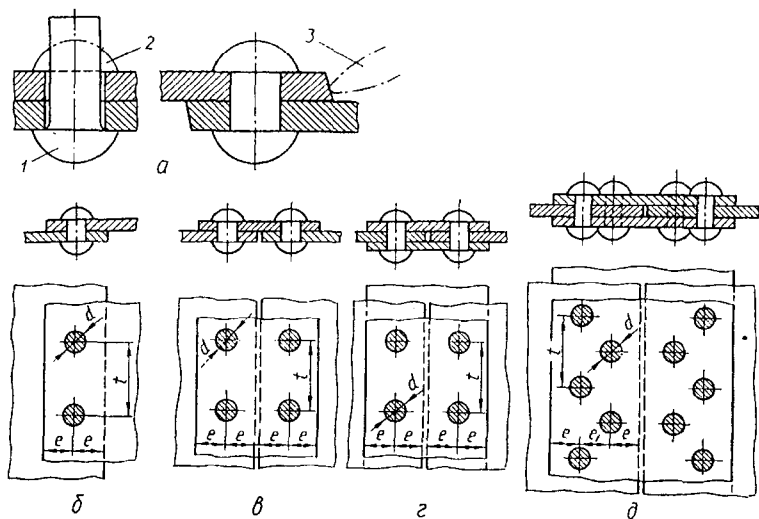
Заклепочные соединения: а – образование заклепочного соединения; б – однорядный шов внахлестку; в – г – однорядный шов встык с двумя накладками; д – двухрядный шов встык с двумя накладками; 1 – заклепка с закладной головкой; 2 – замыкающая головка; 3 – чекан
